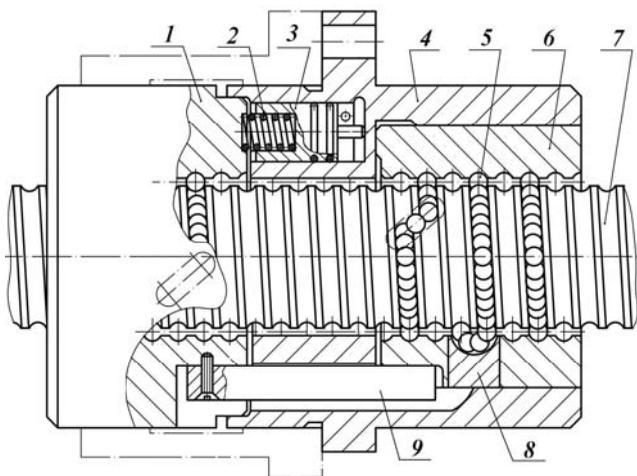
Передача винт-гайка качения с осевым смещением для регулирования натяга обеих гаек 1 и 4 под действием усилия пружины 2 и давления в подпоршневой полости 3
